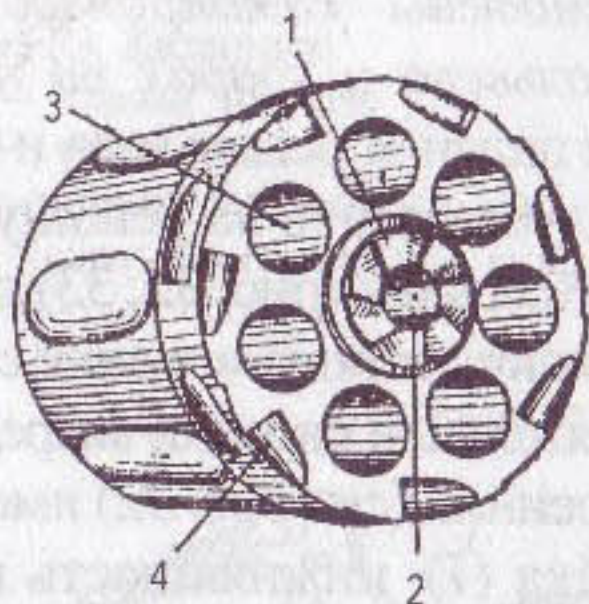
Барабан (вид сзади): 1 — храповое колесо; 2 — центральный канал; 3 — камера; 4 — выемка
